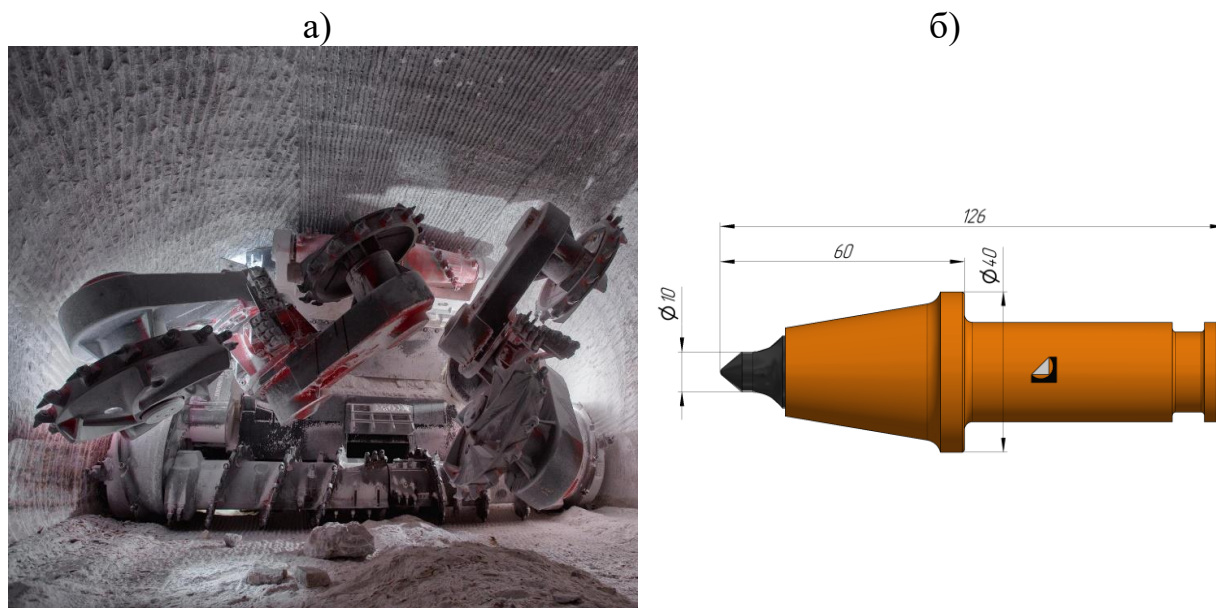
резцы типа РШ: а) РШ, установленные на проходческо-очистном комбайне Урал-20Рс планетарно-дисковым ИО; б) основные конструктивные параметры РШ 25-65L60/18
